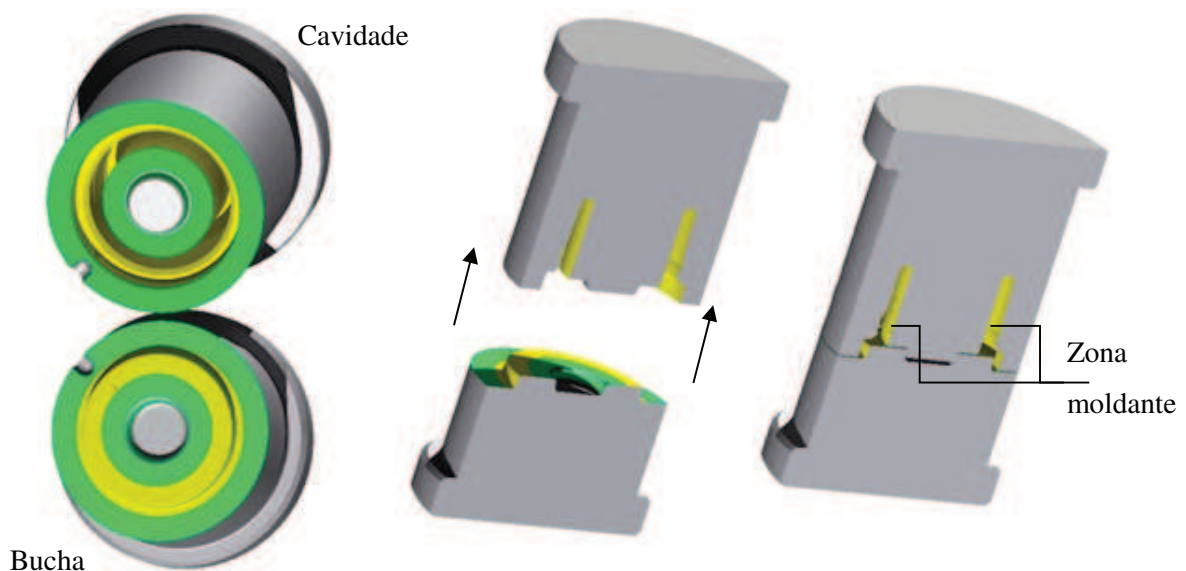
Elementos moldantes (cavidade e bucha): esquema de montagem e ilustração da zona moldante.
